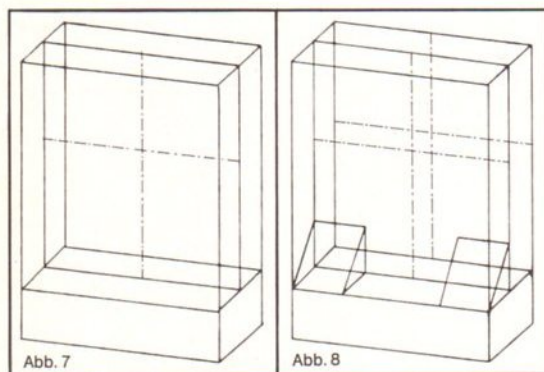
Zweite Bauschicht eingezeichnet. Strichpunktiertes Achsenkreuz, um Mittelpunkt für Bohrung und Rundung festzulegen.
